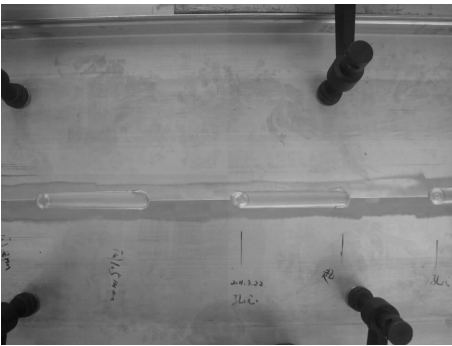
FSW 焊段焊后的 3100mm 的部件照片
